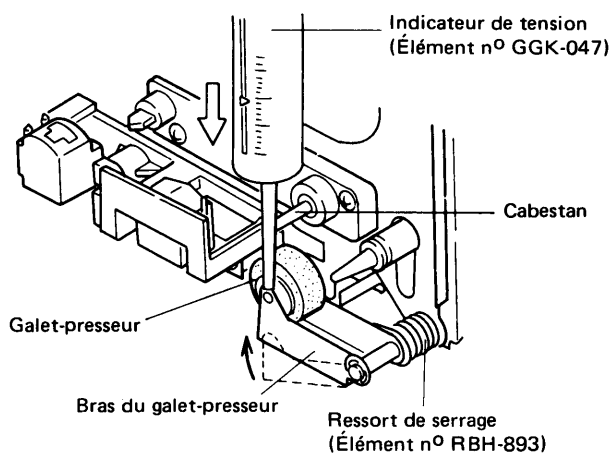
Réglage de la pression du rouleau de serrage.
